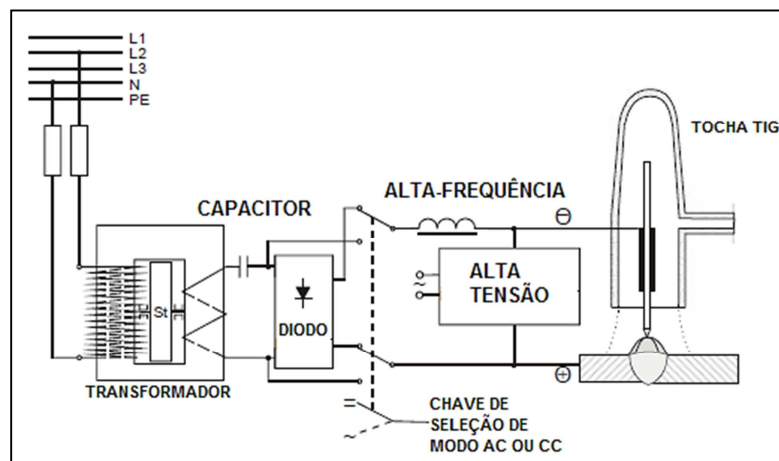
Esquema ilustrativo da máquina de solda referente ao processo TIG (Adaptado de Welding Institute RWTH, Aachen University, Welding Technology Welding and Cutting Technologies).
